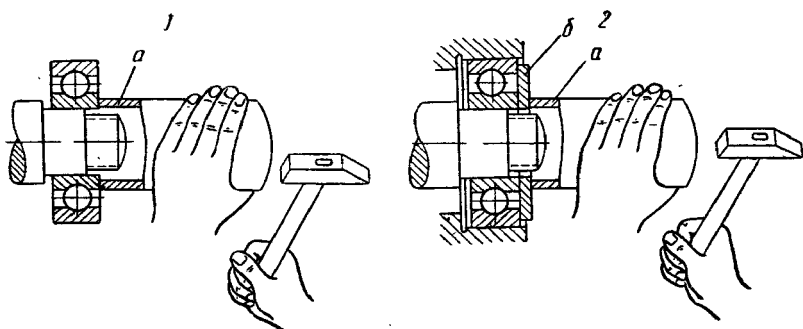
Насадка шариковых подшипников на шейки вала и в корпус:
